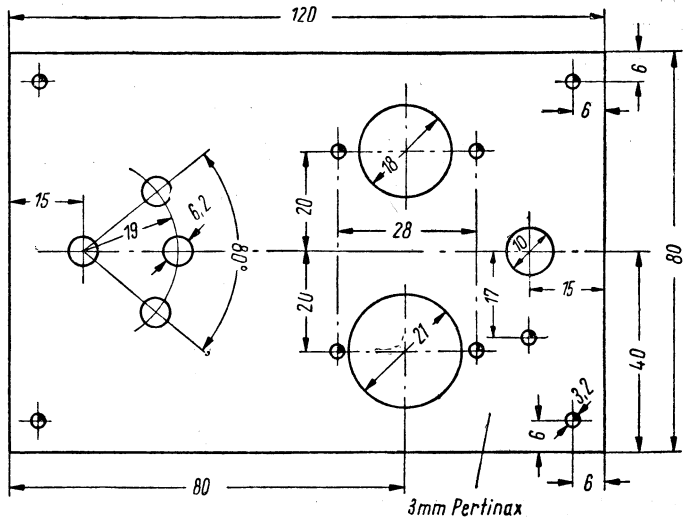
Maßskizze für die Frontplatte des Durchgangsprüfers
